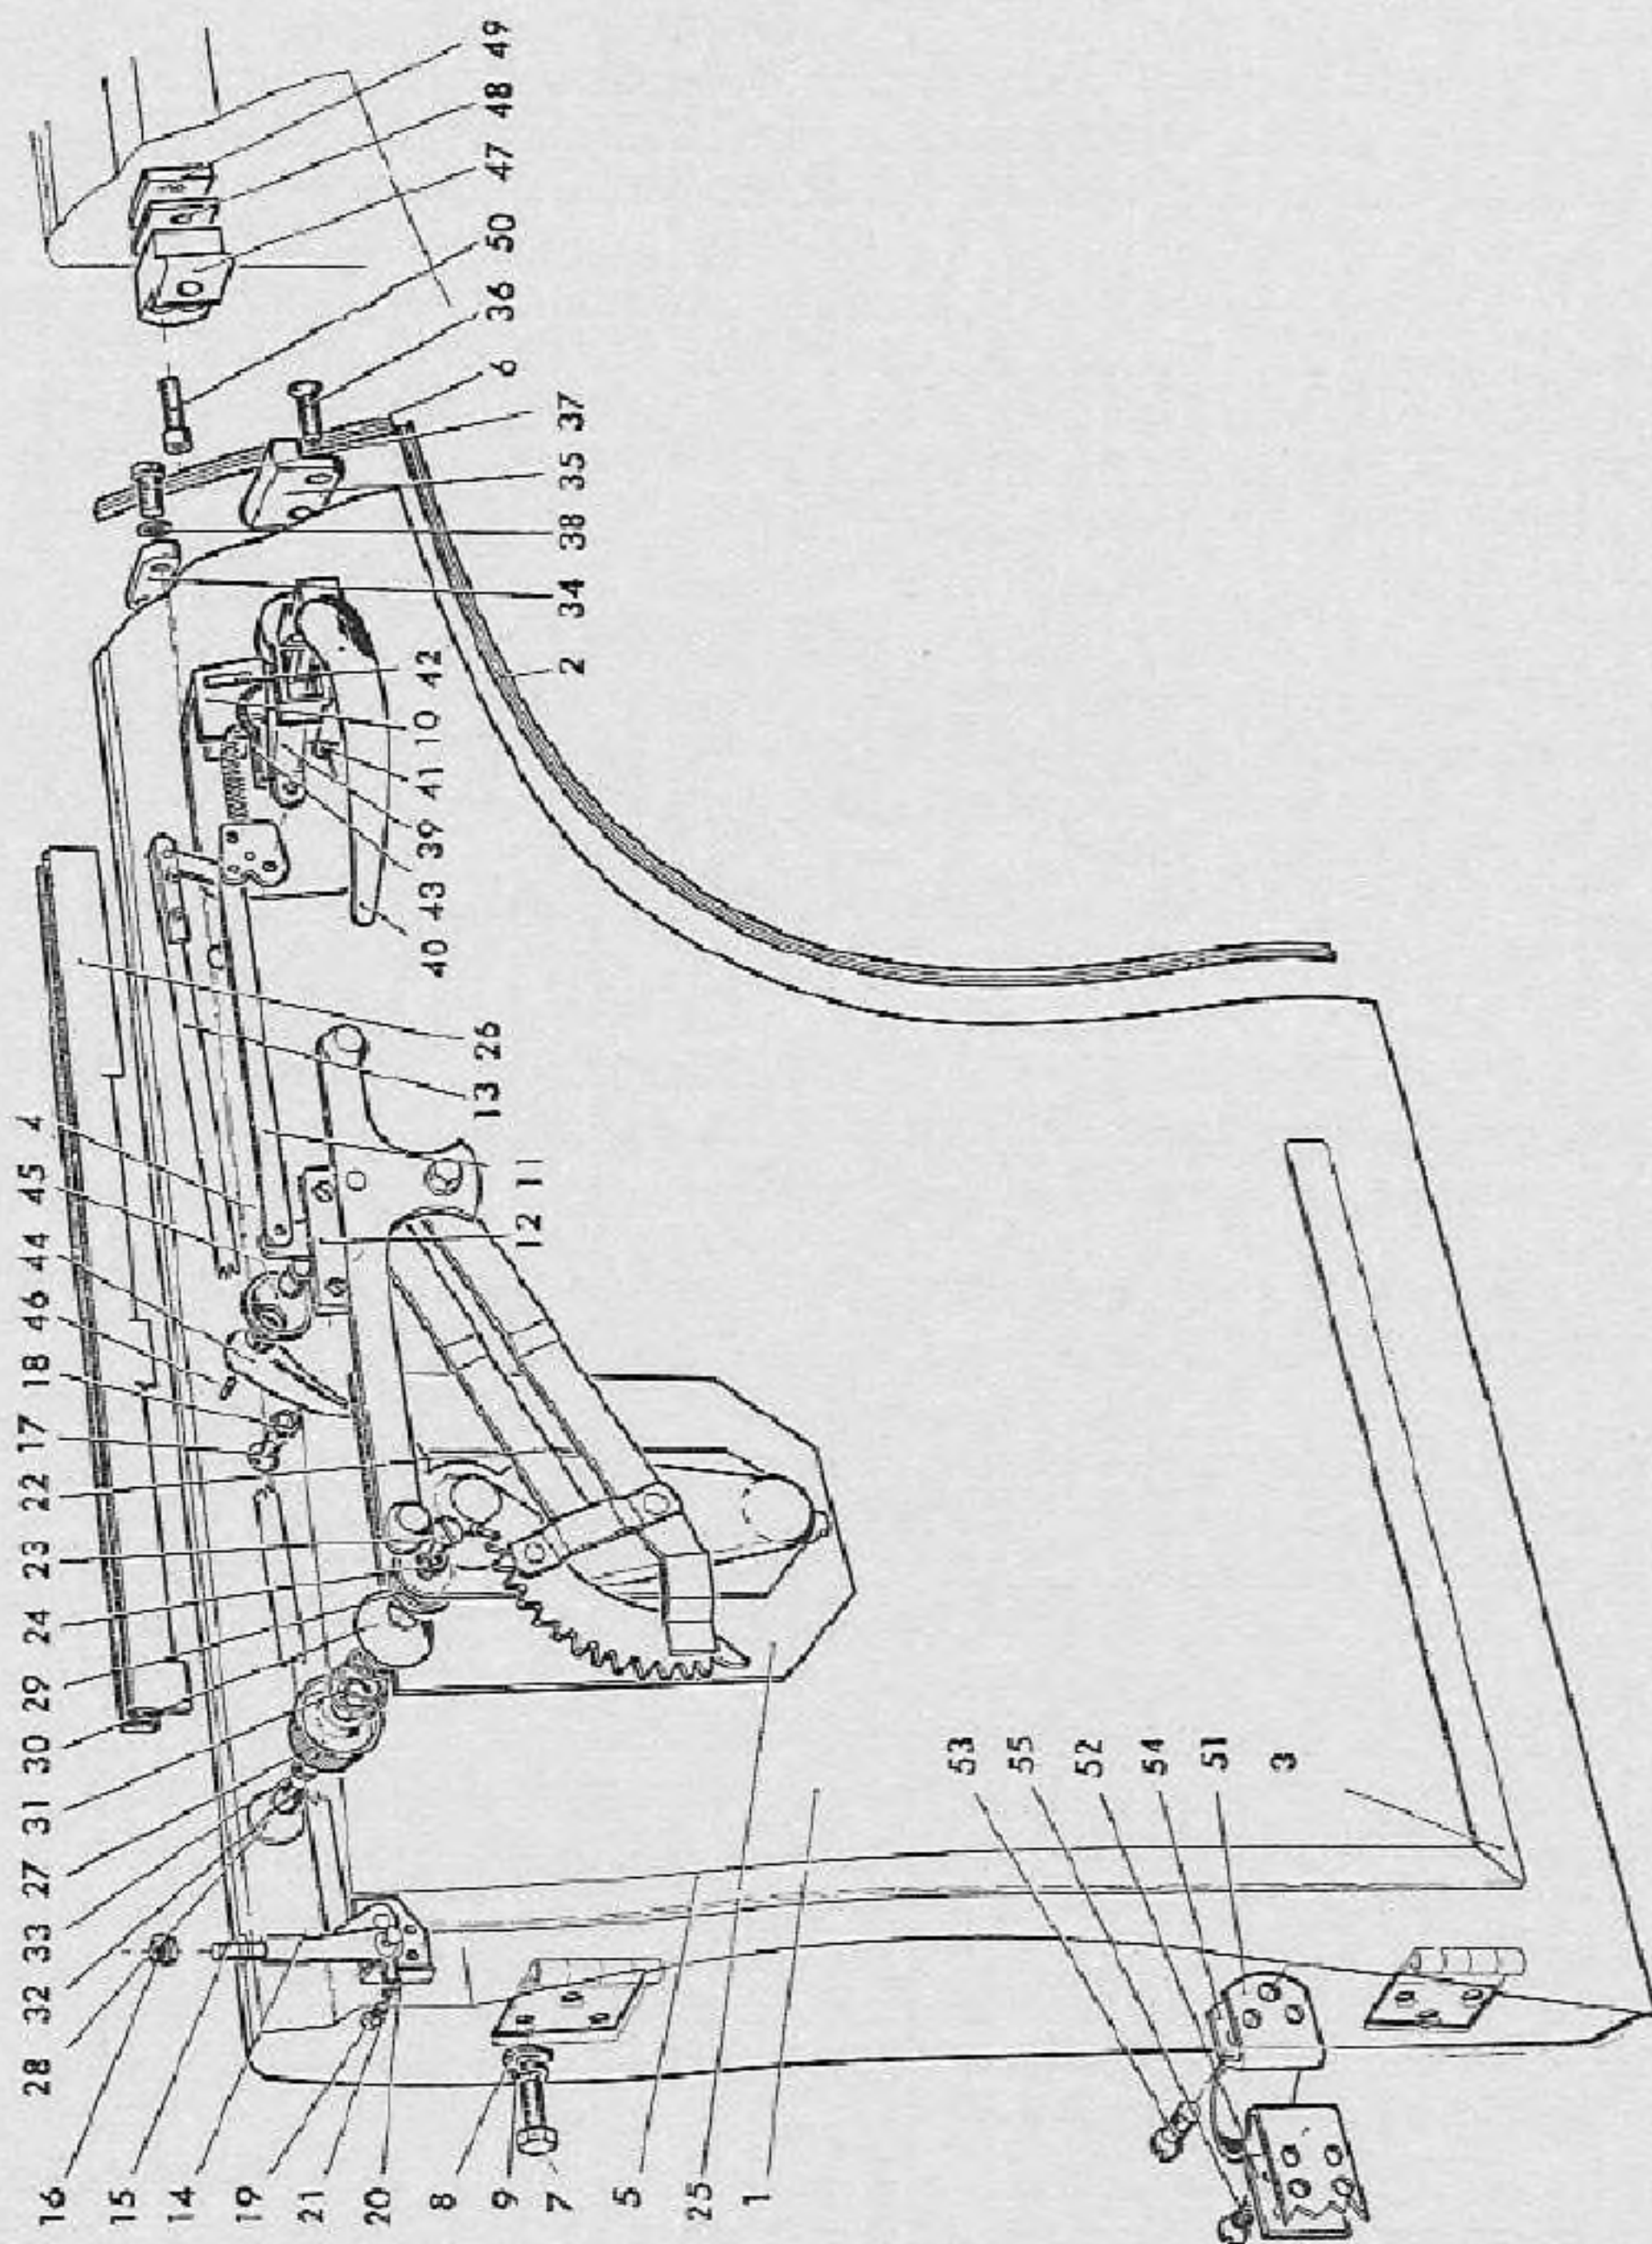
Puerta trasera izquierda del Sedan AU 1000 4p.
